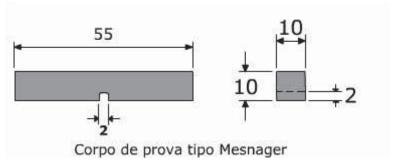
Ilustração sobre corpos de prova Fonte: (CIMM, 2008).
